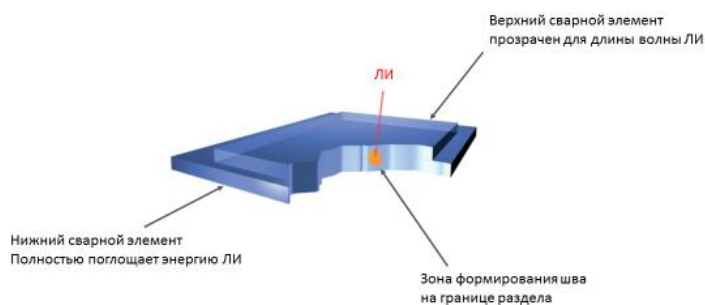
Схема процесса лазерной сварки полимерных материалов
